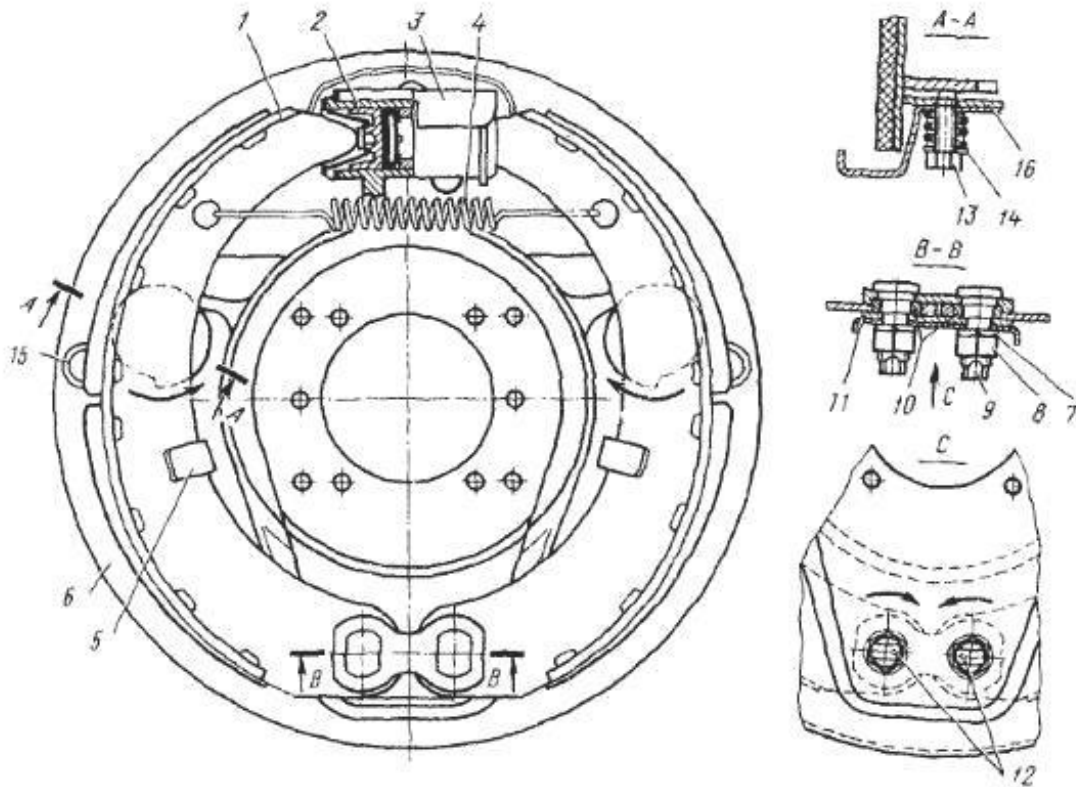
Тормозной механизм колеса ГАЗ-3507
